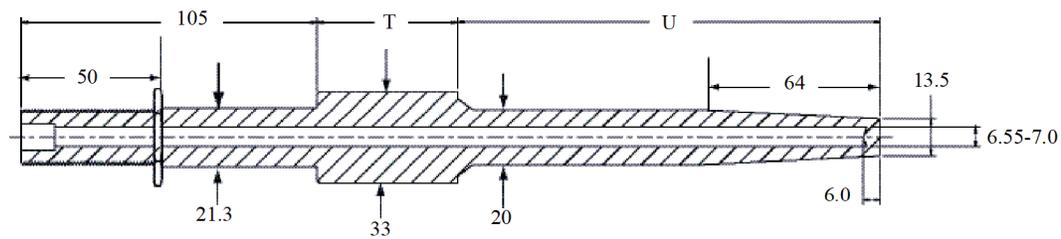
Schutzrohr aus Vollmaterial mit Flansch (3 mm)
